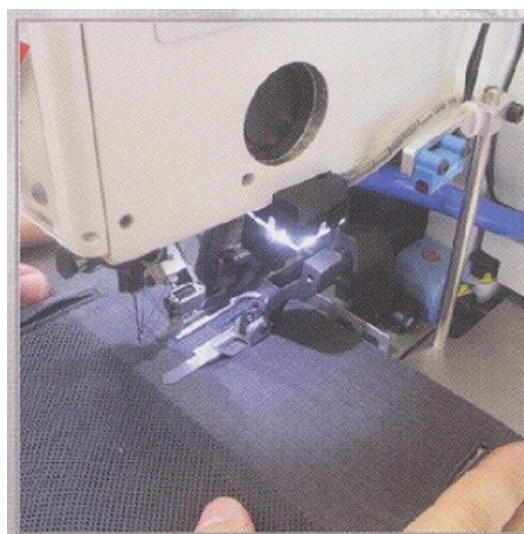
/5 - kleštiny k držení horní nitě [2]
